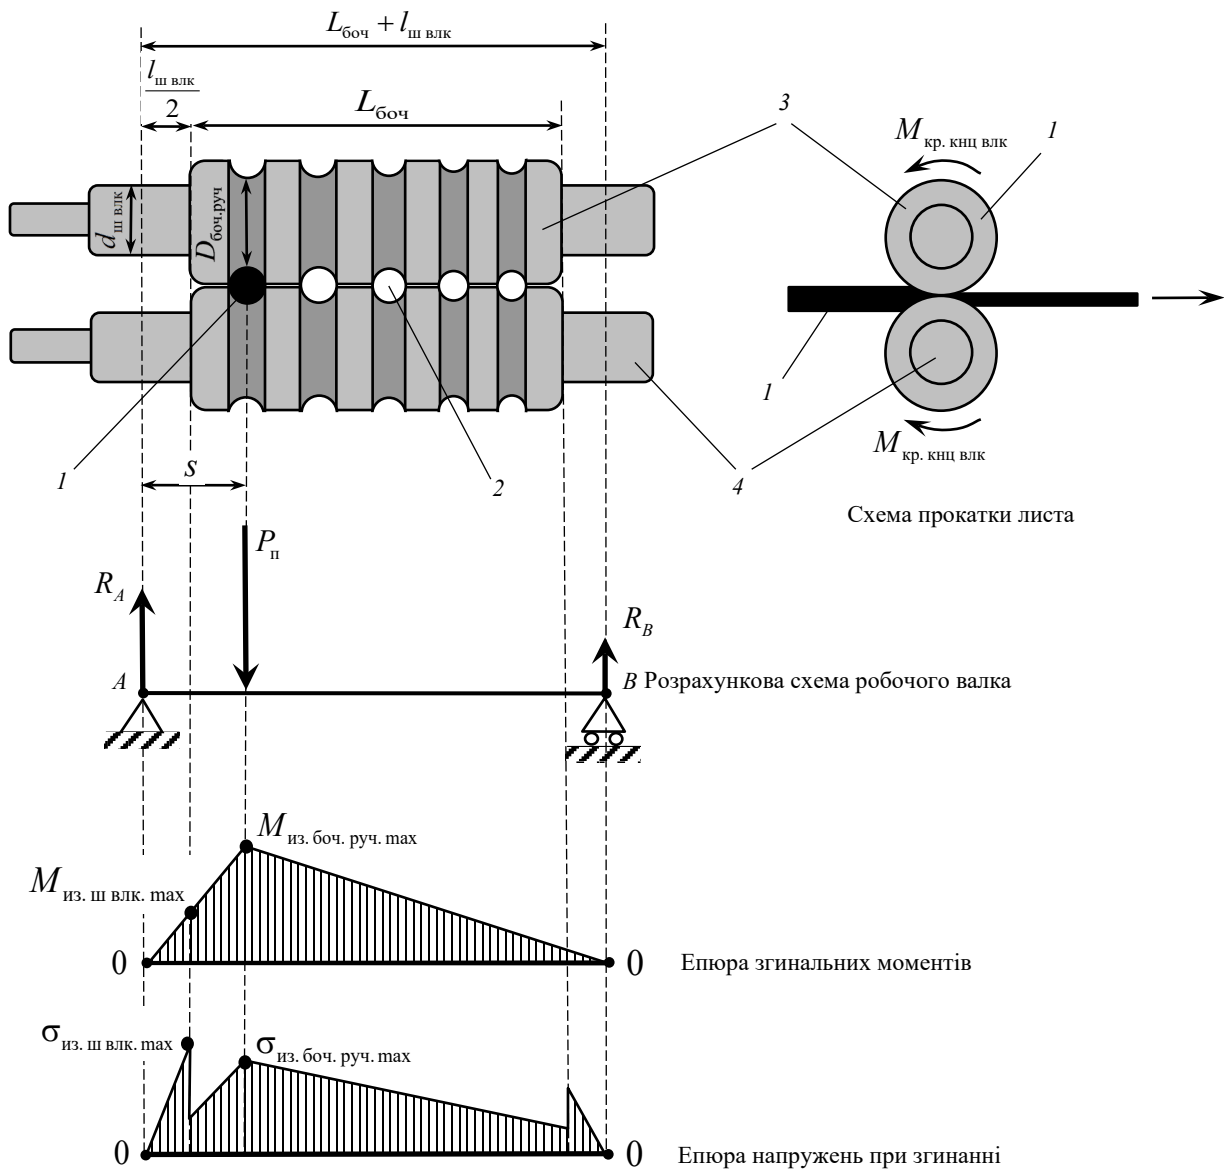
Схема до розрахунку каліброваного валка: 1 — сортова заготовка; 2 — середній калібр; 3, 4 — бочка і шийка робочого валка s — відстань від осі калібру до осі натискного гвинта; R_A, R_B — опорні реакції в точках A и B ; $M_{\text{из. боч. руч. max}}$ — максимальний згинальний момент, що діє в небезпечному перетині бочки по дну рівчака; $\sigma_{\text{из. боч. руч. max}}$ — максимальне нормальне напруження
